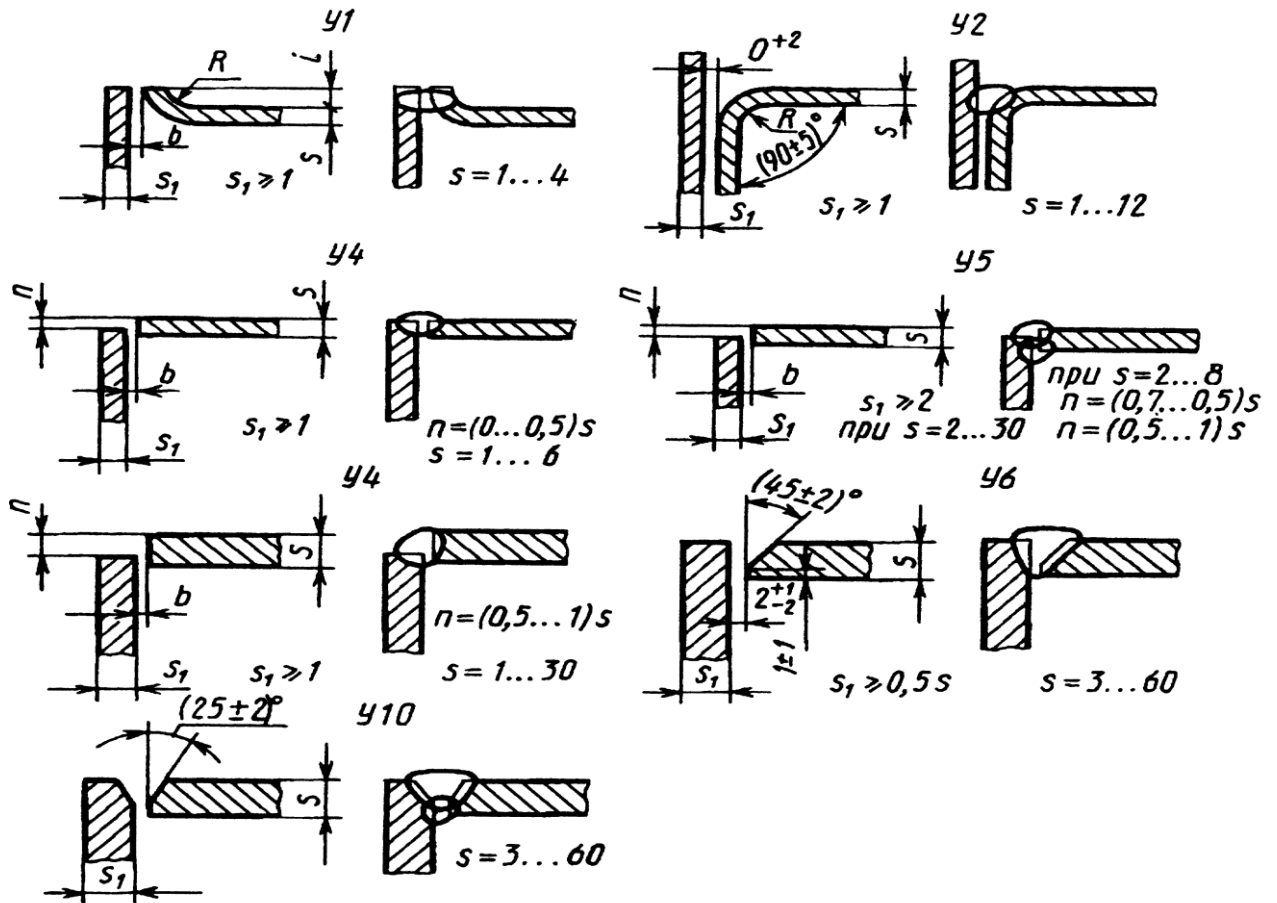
Форма поперечного сечения подготовленных кромок с размерами и сварного шва, а также стандартные условные обозначения угловых - Y1...Y10 сварных соединений.
